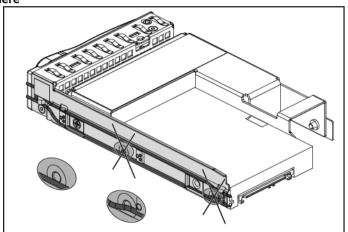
Retrait et installation d'un assemblage de la carte du support de disque dur
